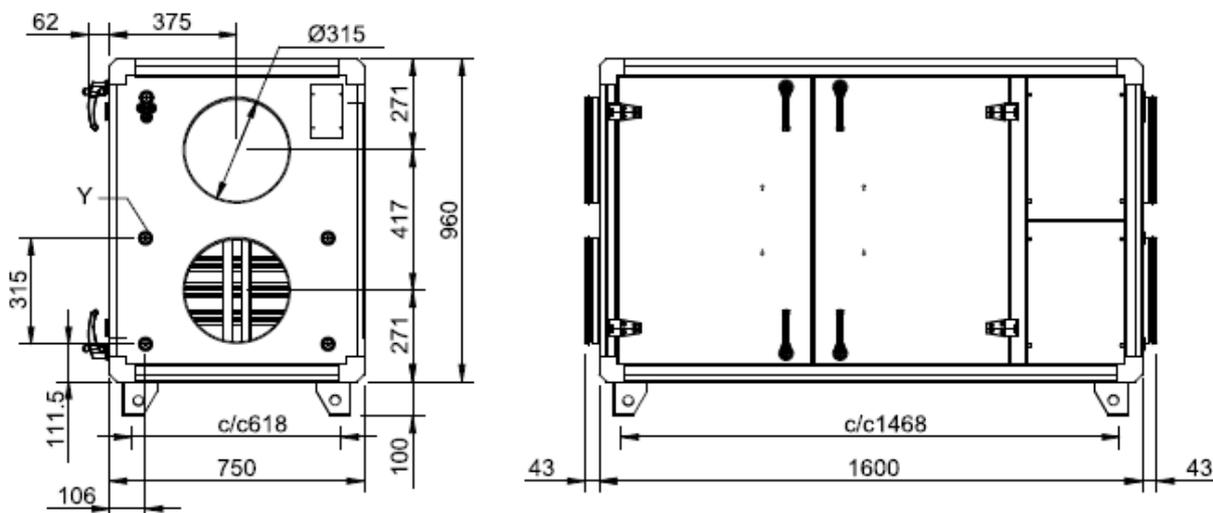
Dimensioni (mm) SR03 (ingresso aria lato DESTRO)
